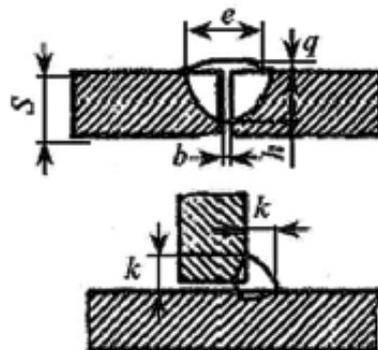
Основные геометрические параметры сварных швов:
